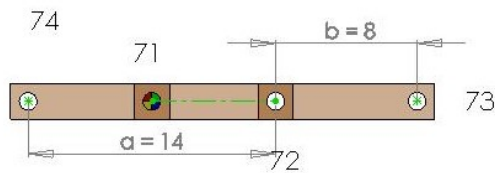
Imagen de la pieza 7 del mecanismo a-z-1133
